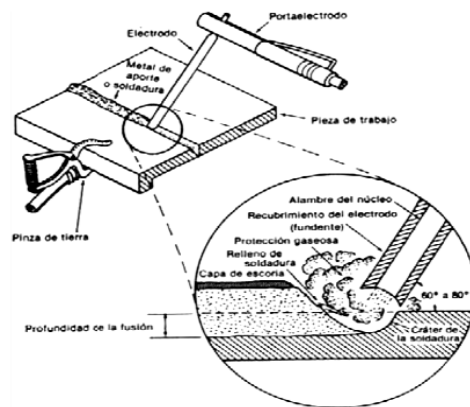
2 Esquema de soldadura por arco manual con electrodo revestido [4].
